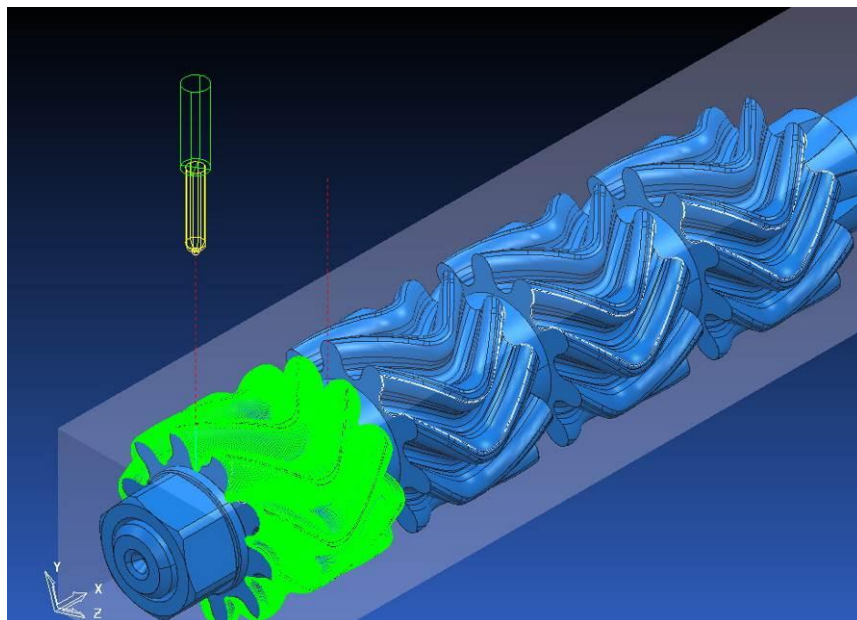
Комп'ютерна імітація фрезерування шевронних зубчастих коліс в Autodesk PowerMill [291]
